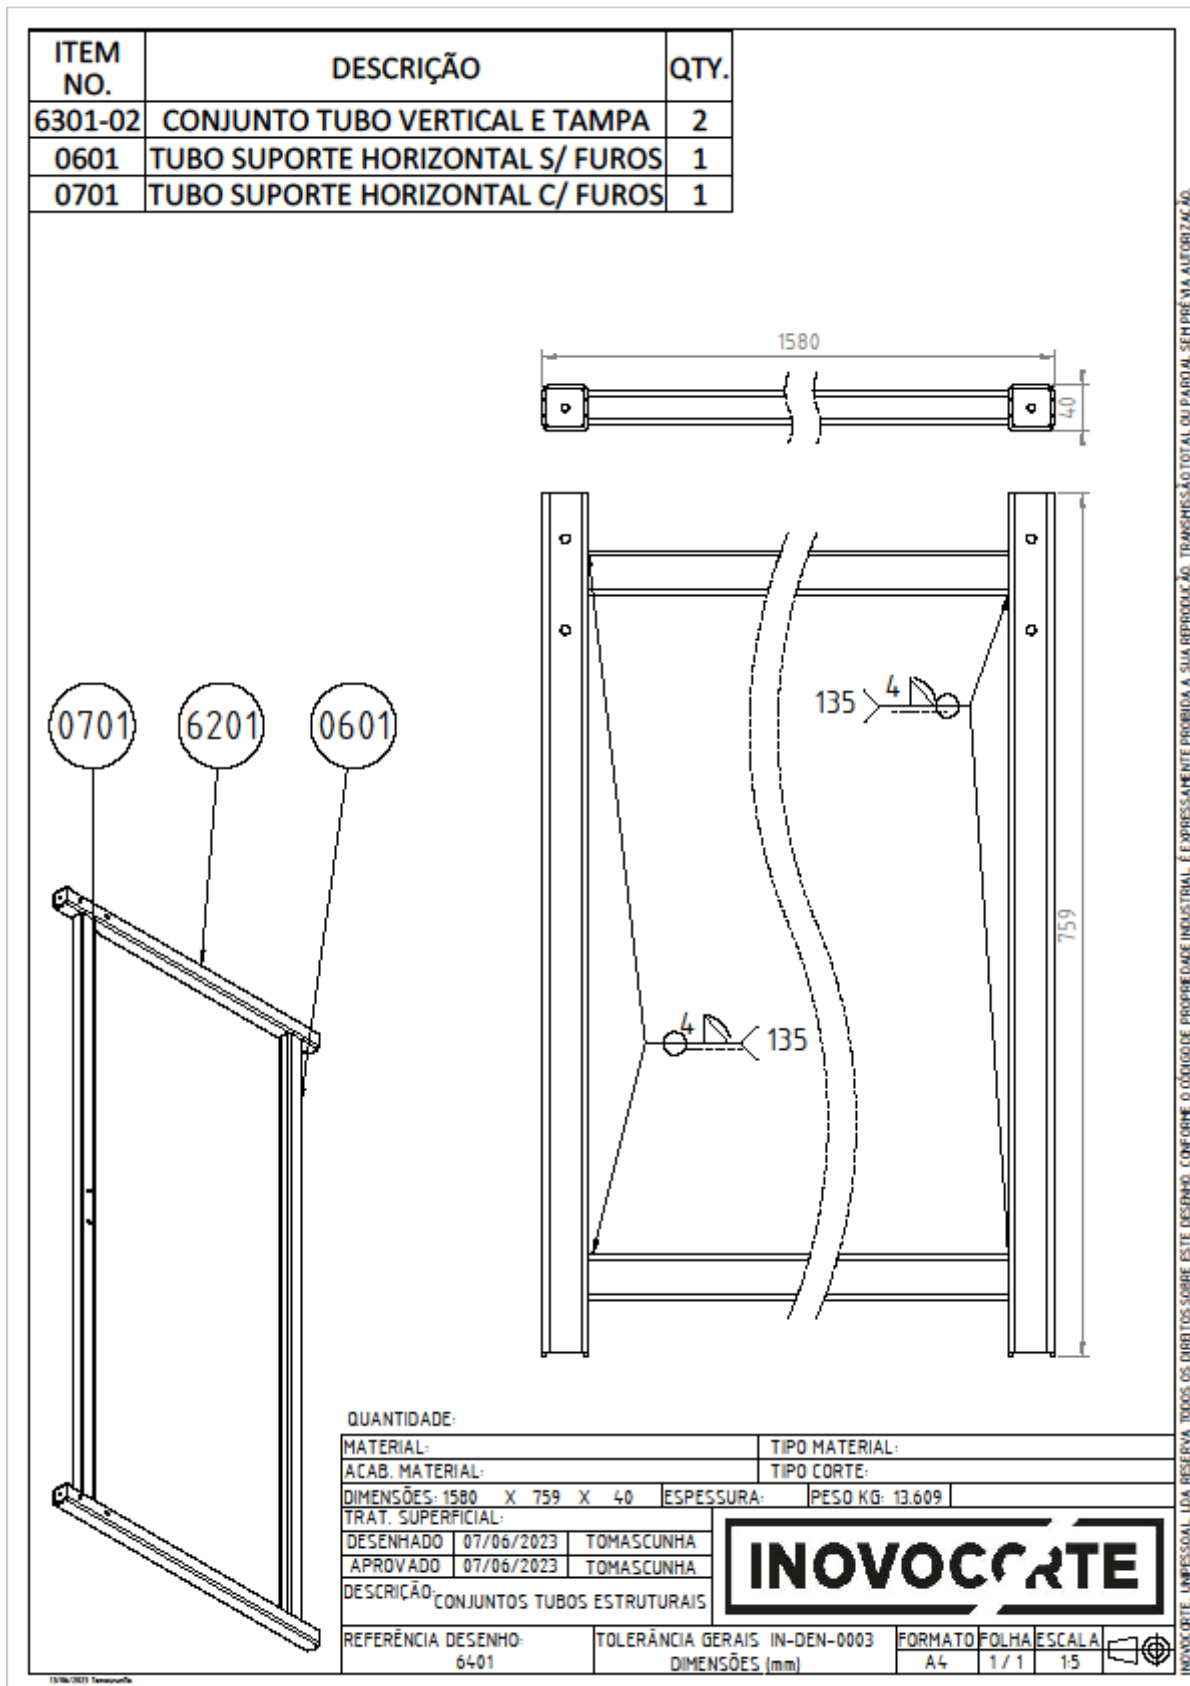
Desenho técnico do conjunto tubos estruturais (6401).
